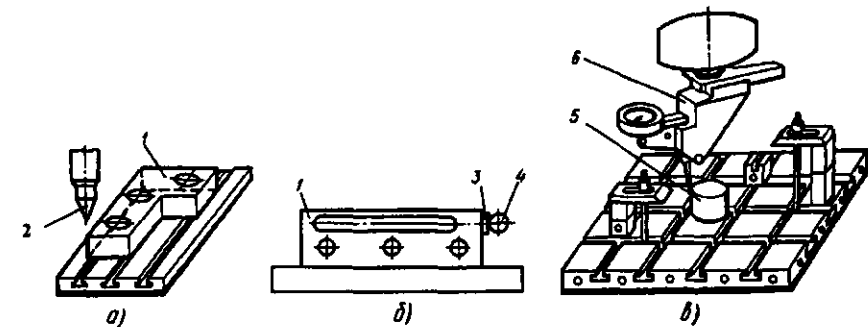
Способы наладки нулевого положения: а – по боковой поверхности с помощью центра; б – по боковой поверхности с помощью контрольной оправки; в – по пальцу с помощью центроискателя; 1 – заготовка; 2 – центр; 3 – мерная плитка; 4 – контрольная оправка; 5 – установочный палец; 6 – центроискатель
